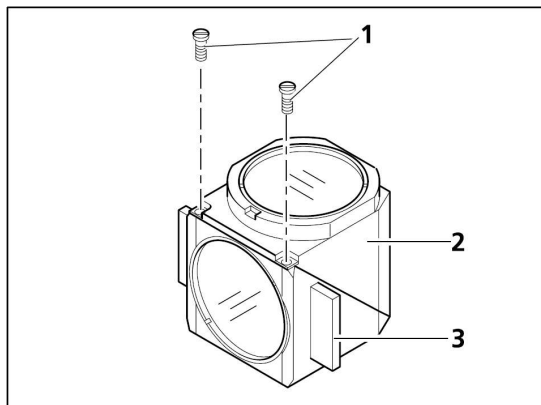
Montáž filtrů a děliče barev (světelného svazku)
